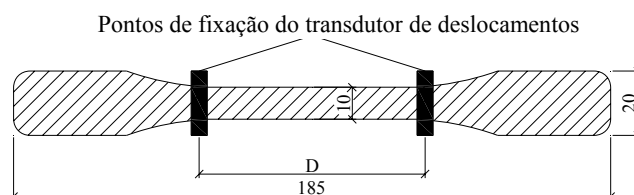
Geometria dos provetes de adesivo (dimensões em mm)
